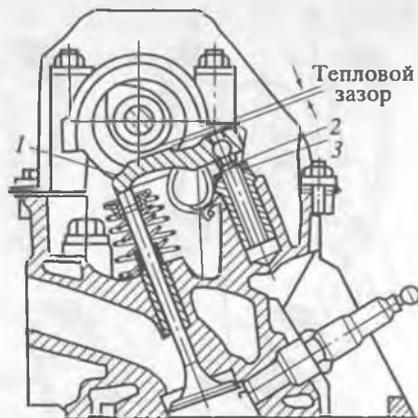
Регулировка тепловых зазоров газораспределительного механизма автомобиля ВАЗ классической компоновки
